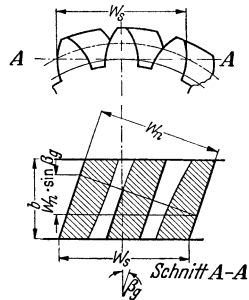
Zahnweiten-Messung am Schrägzahnrad.
